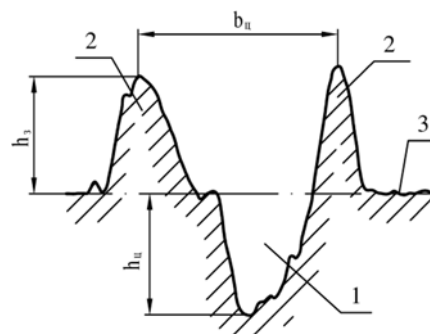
Форма поперечного сечения микроцарапины, полученной при микроцарапании поверхности образца напыльем металла с одинаковой высотой режущих кромок
